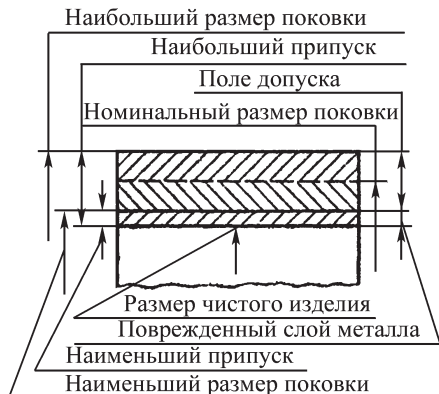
Схема расположения припусков и допусков на поковке
